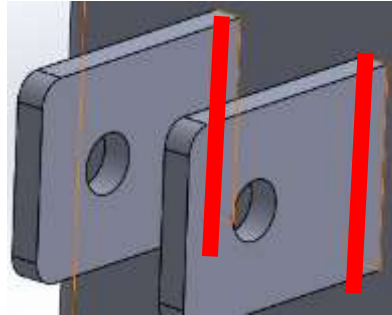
Localización de la soldadura en las orejas de sujeción del actuador
